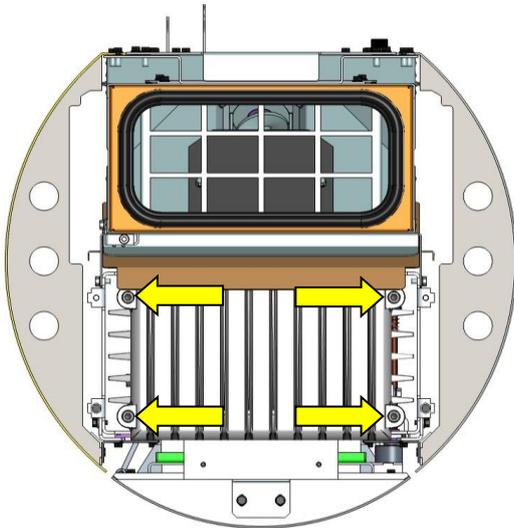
démontage du couvercle en fonte Montreal.nrg
